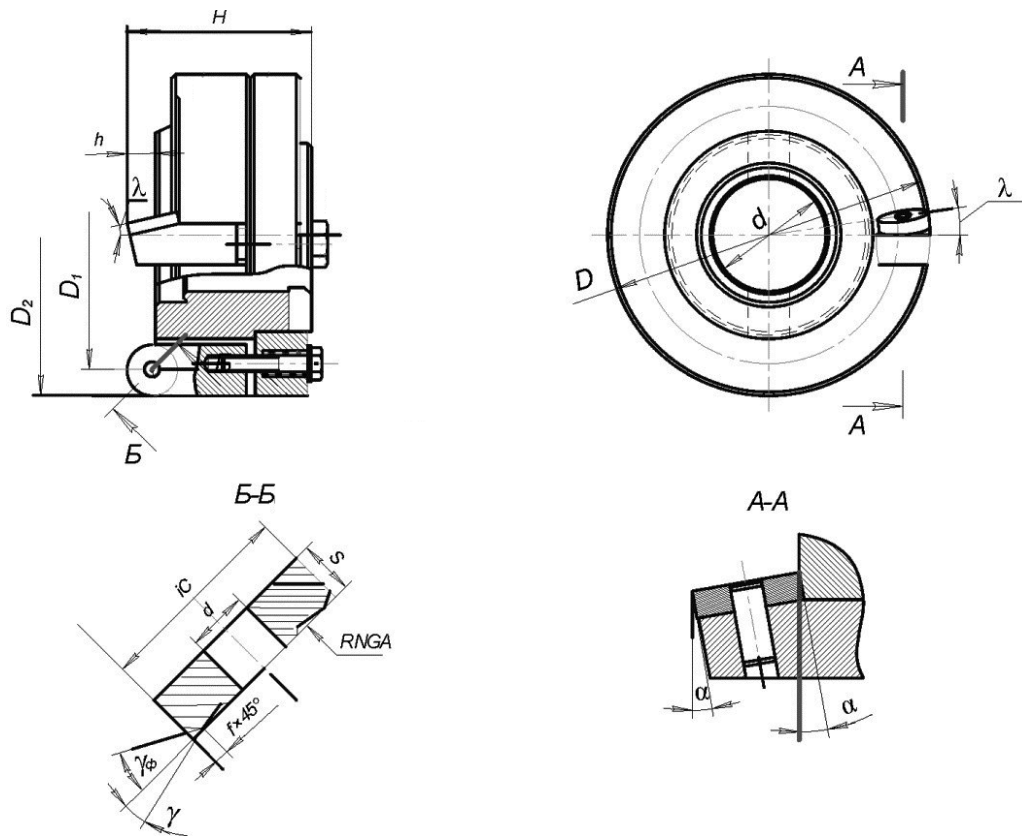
Фреза торцева, оснащена твердосплавними ЗБП
